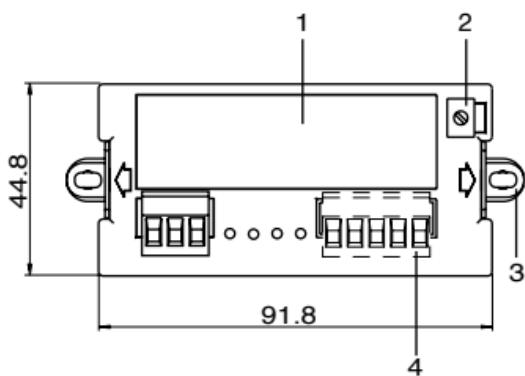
Rückansicht mit eingesetzten Spindeln und Klammern
